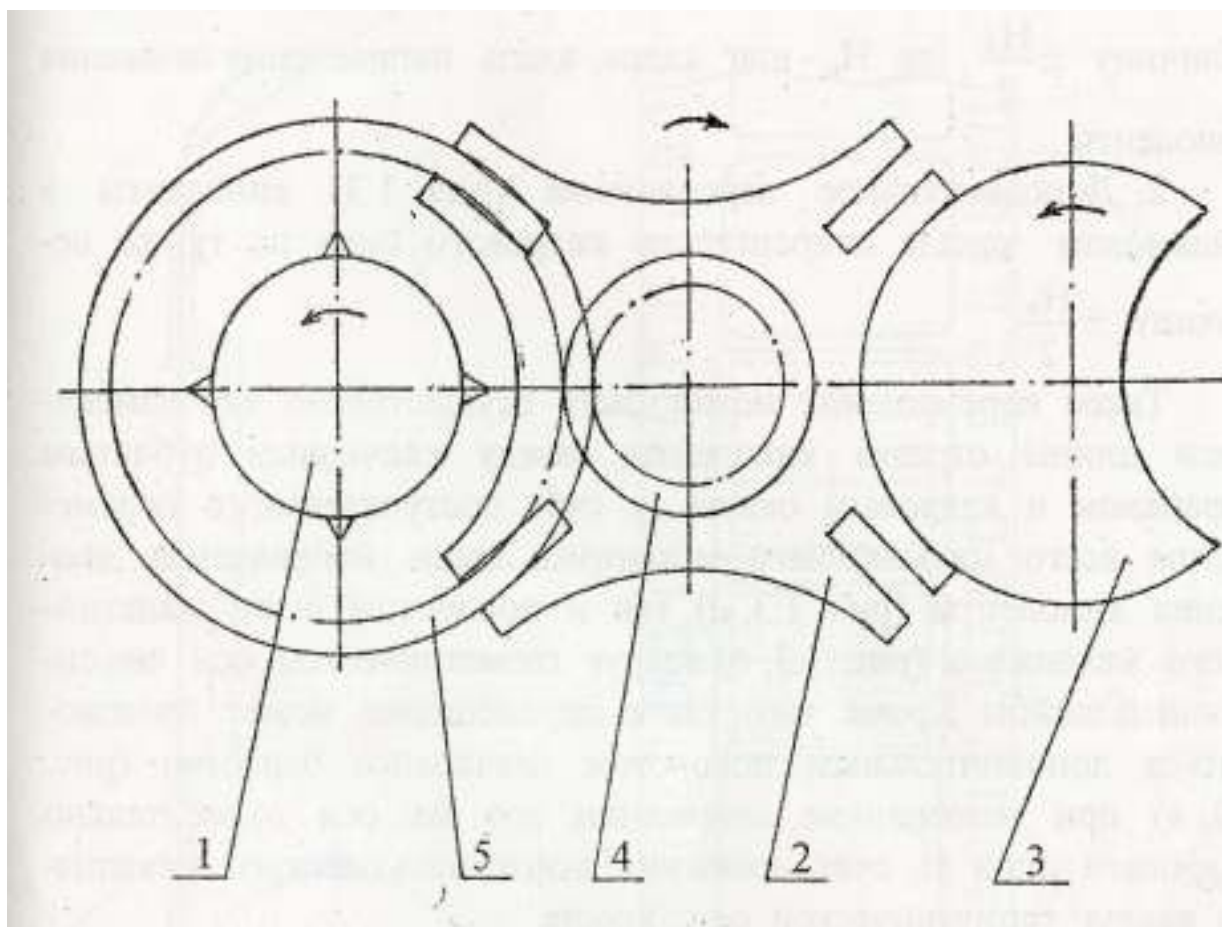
Схема передачи движения скачковому зубчатому барабану через редуктор:
